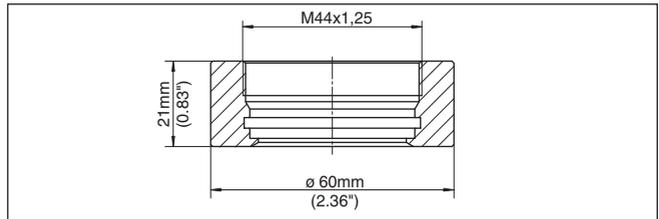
Dimensions raccord à souder M44 x 1,25 VEGABAR 82, 83
